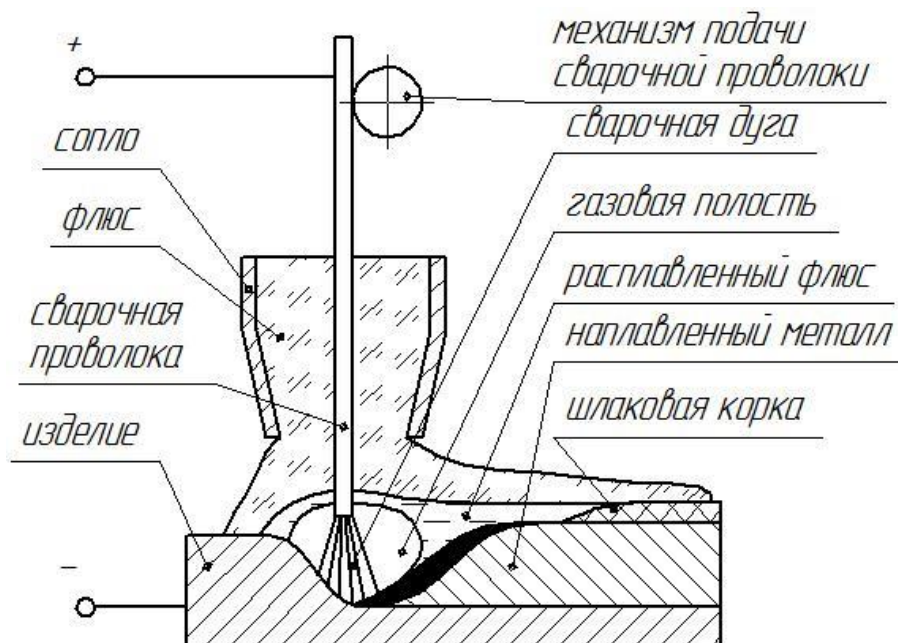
Схема выполнения наплавки под слоем флюса
